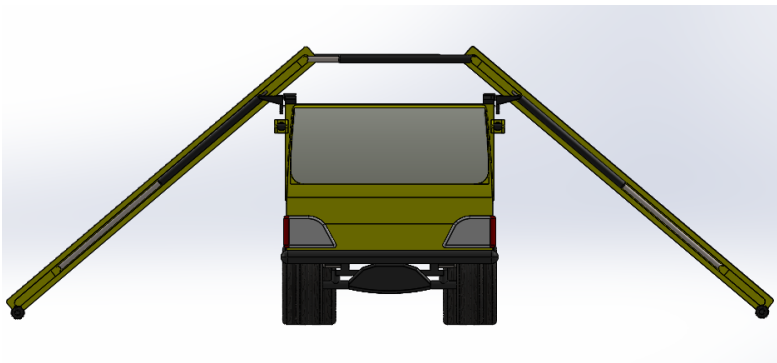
24 Tampak Isometris (Dudukan Konveyor
